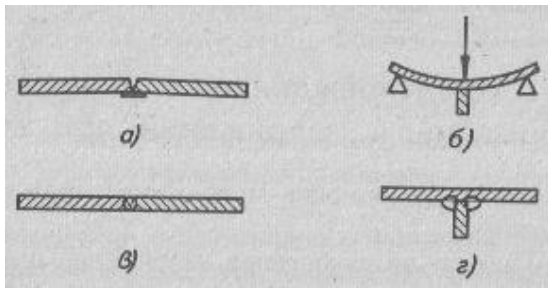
Методы подготовки конструкции к сварке: а — обратный прогиб; б — обратная деформация; в и г — конструкции после сварки
